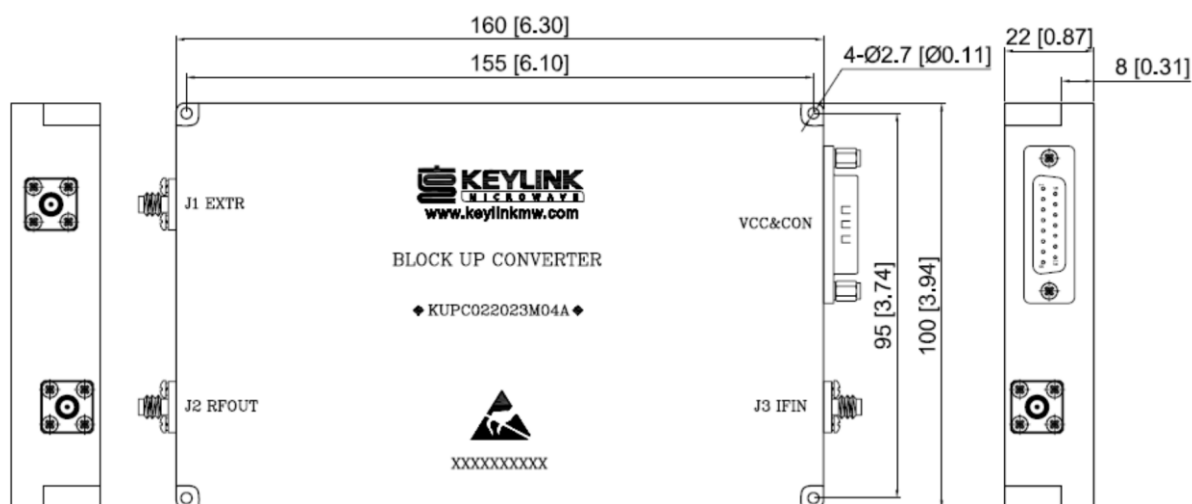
Внешний вид РЧ модуля KUPC02203M04A с указанием габаритных размеров
